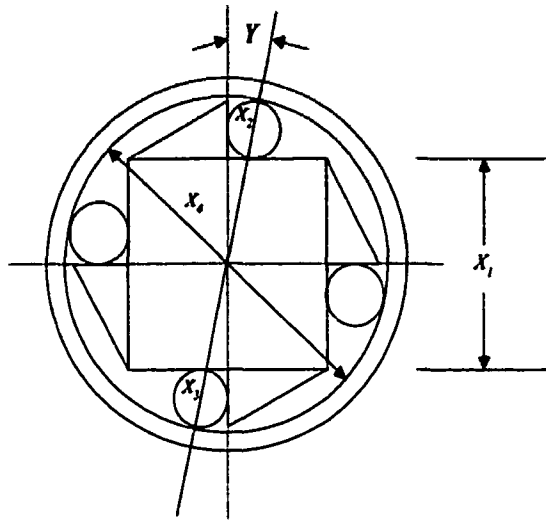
Exemple d'assemblage d'un cas non linéaire
